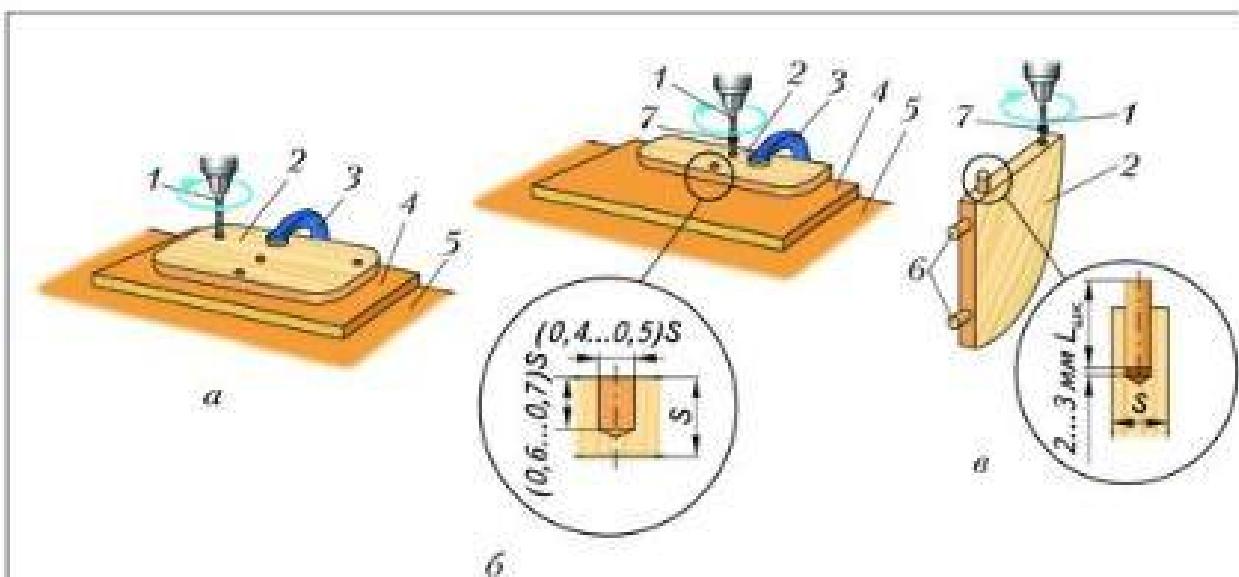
Сверление отверстий в деталях: а – в основании; б – в полочке; в – в кронштейне; 1 – сверло; 2 – заготовка; 3 – струбцина; 4 – подкладная доска; 5 – верстак; 6 – шканты; 7 – ограничитель (резиновая втулка)
